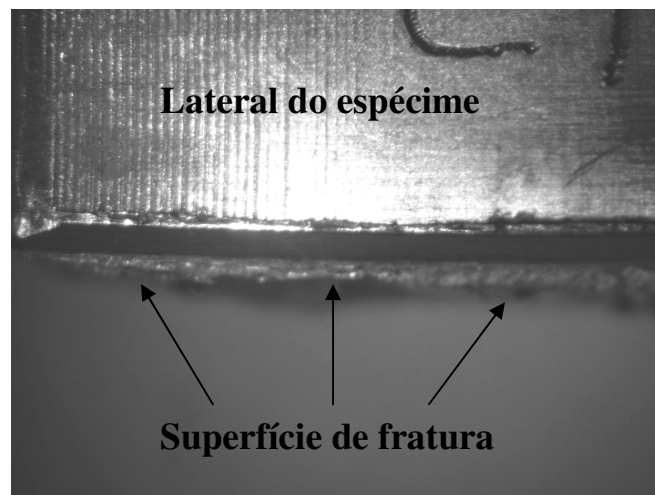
Vista perpendicular à superfície de fratura de espécime SE(T) com trinca rasa, com entalhe lateral, CTR06-EL-NV
